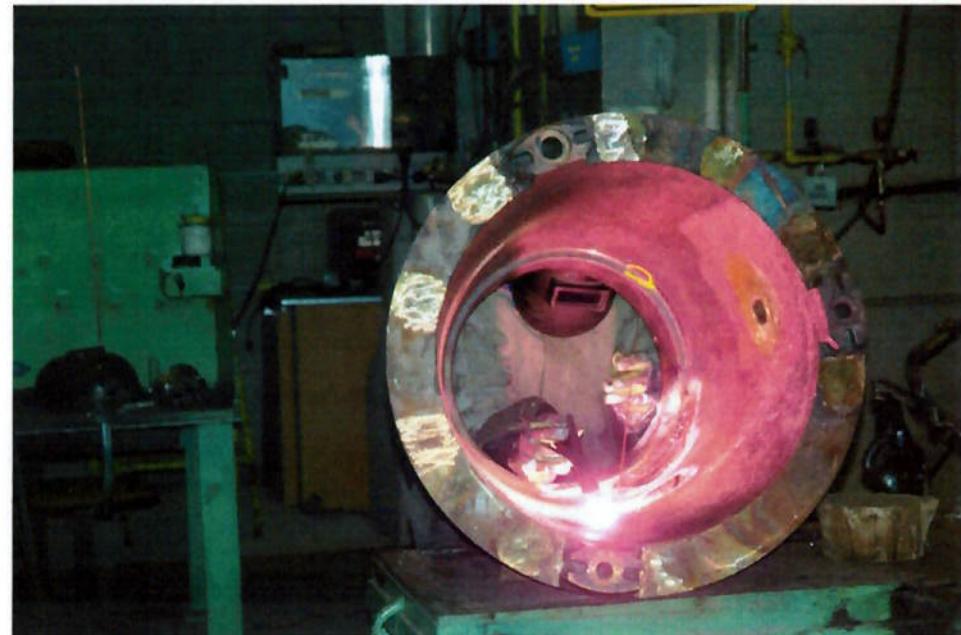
Exemplo do Setor de Soldagem de Materiais Não Ferrosos.
